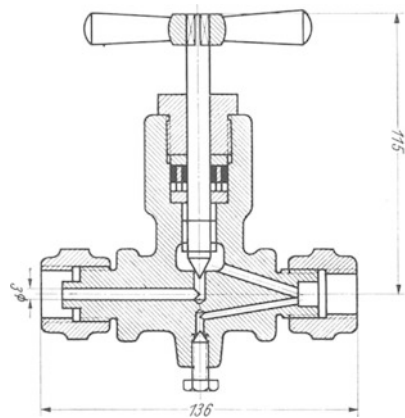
Absperrung für Manometer an Pumpenkörpern und Steuerungen. (Schwietzke, Düsseldorf.)
